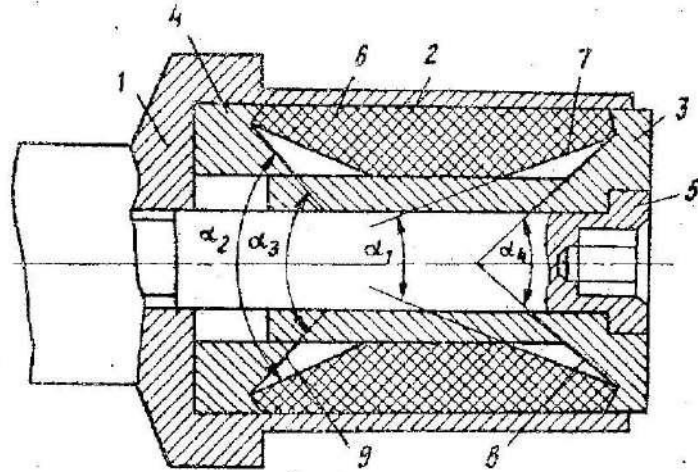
Оправка с упругодеформируемым эластичным элементом для закрепления тонкостенных цилиндрических заготовок [11]: 1 – корпус, 2 - тонкостенная рабочая часть корпуса, 3и 4 – втулки, 5 – винт, 6 - упругодеформируемый эластичный элемент
